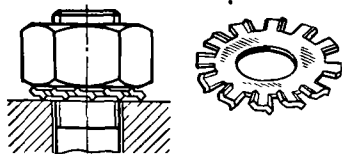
Стопорение гайки храповой шайбой с наружными зубцами
